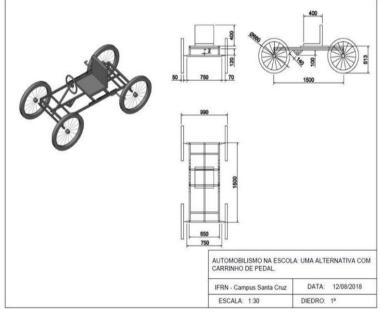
Desenho técnico do kart, projetado através do software AutoCad.
